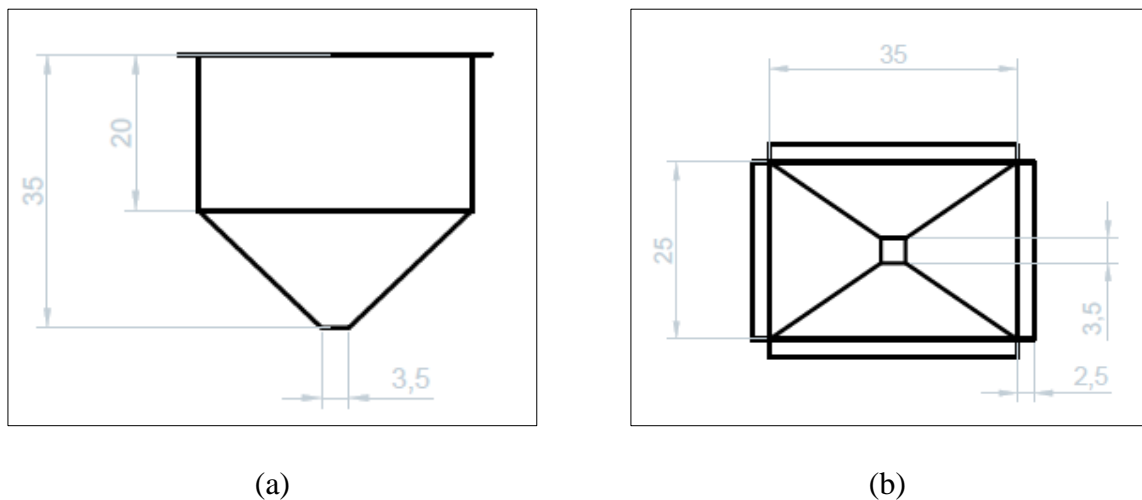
Dimensiones (en cm) del tanque de recirculación.
